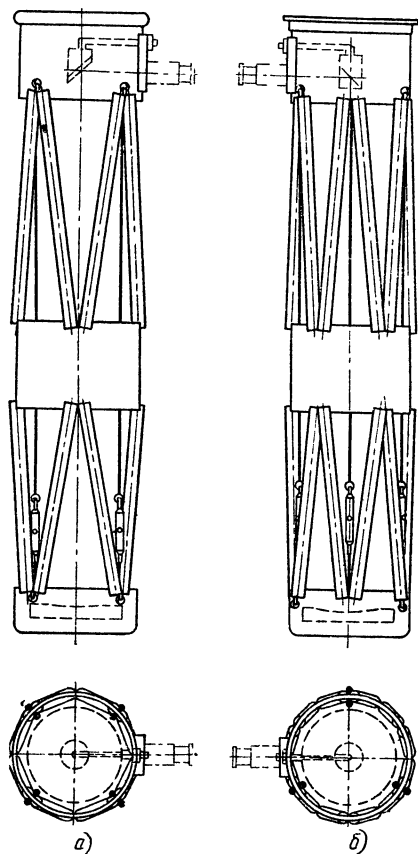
Варианты трубы-каркаса, а — с четырехпарной системой распорок; б — с шестипарной системой распорок.
